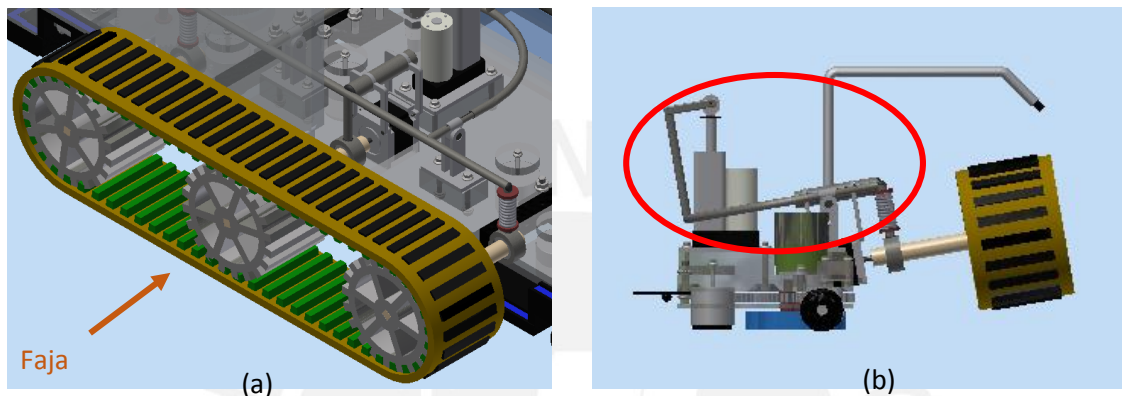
Rodamiento oruga y mecanismo de levantamiento de rodaje
